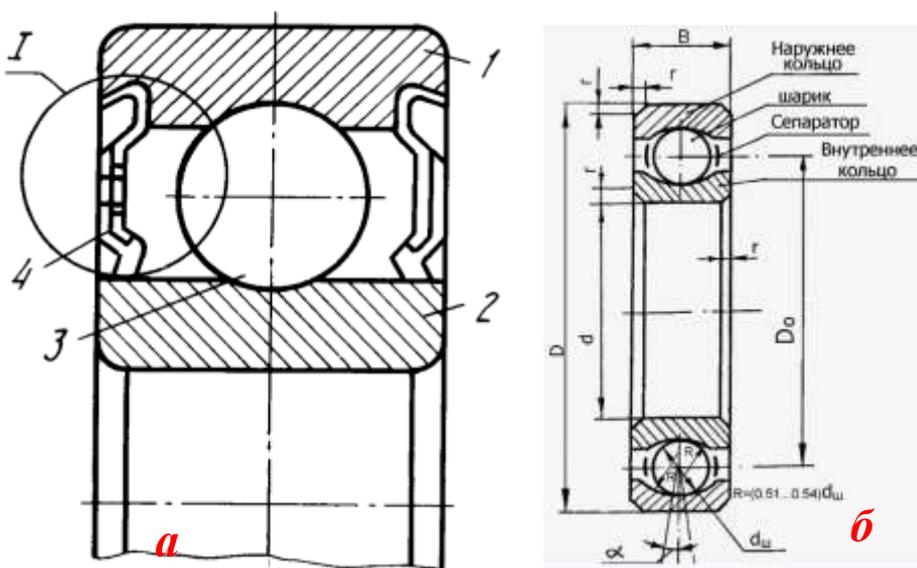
Подшипник шариковый радиальный однорядный с защитными шайбами (а) и открытое (б)
